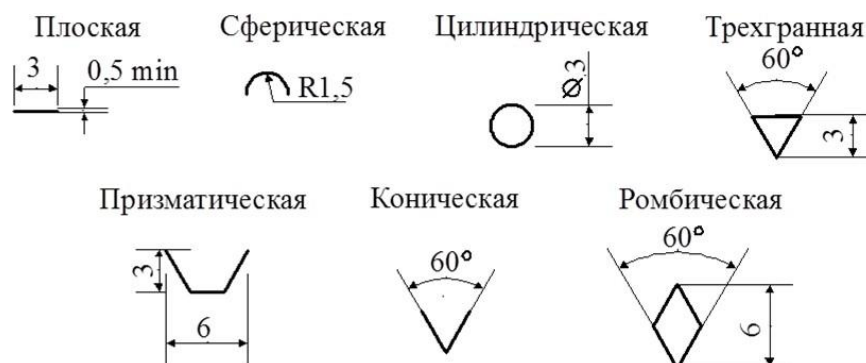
Условное обозначение форм рабочих поверхностей установочных элементов приспособлений
